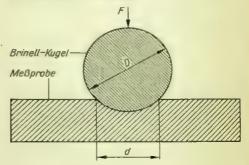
Härteprüfung nach dem Brinellverfahren
